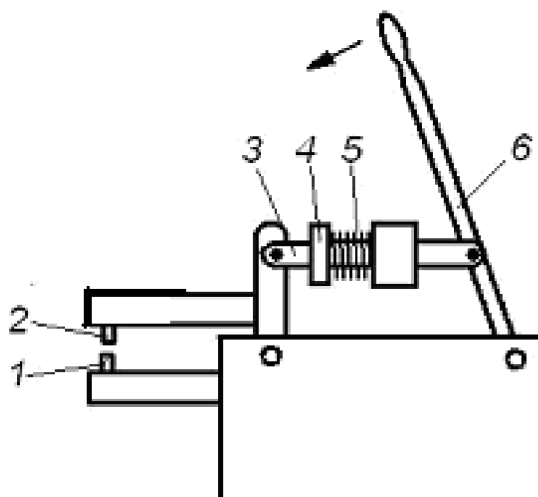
Конструктивная схема машины для точечной сварки.
